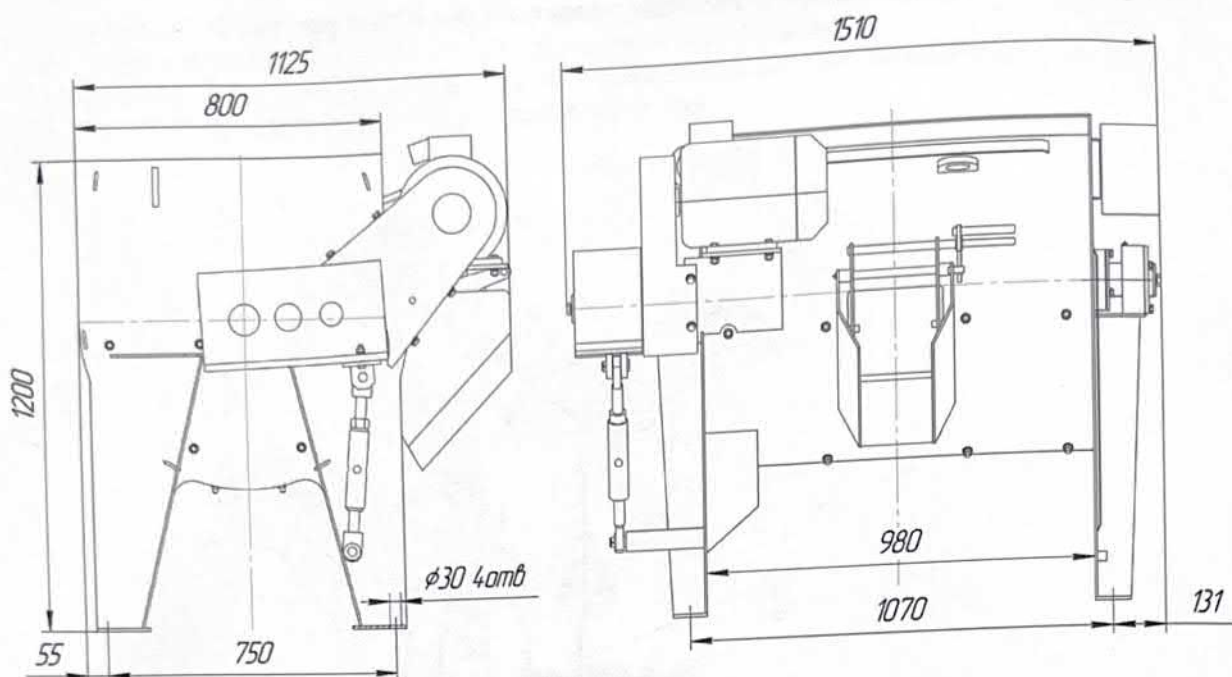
Габаритно-присоединительные размеры СГ-350.
